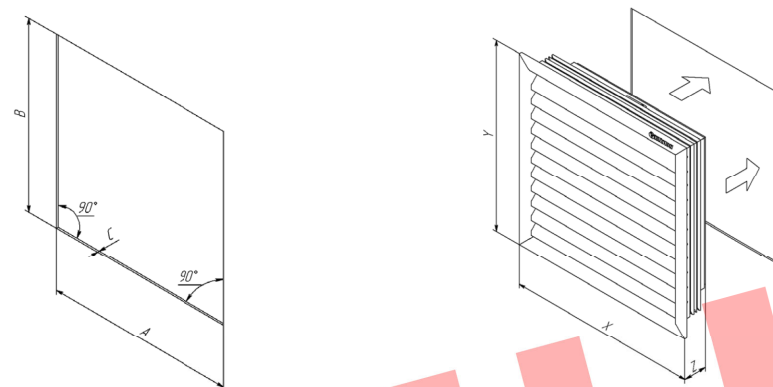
Монтажный вырез и габаритные размеры ФТШ
